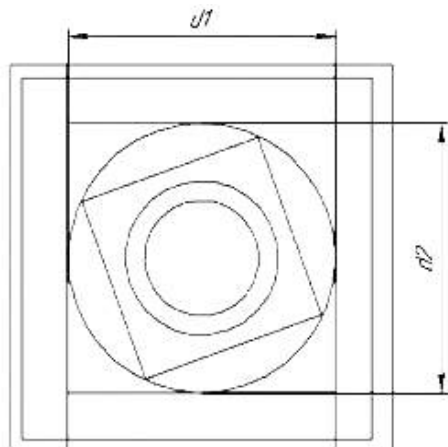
Схема вимірювання зовнішньої циліндричної поверхні
